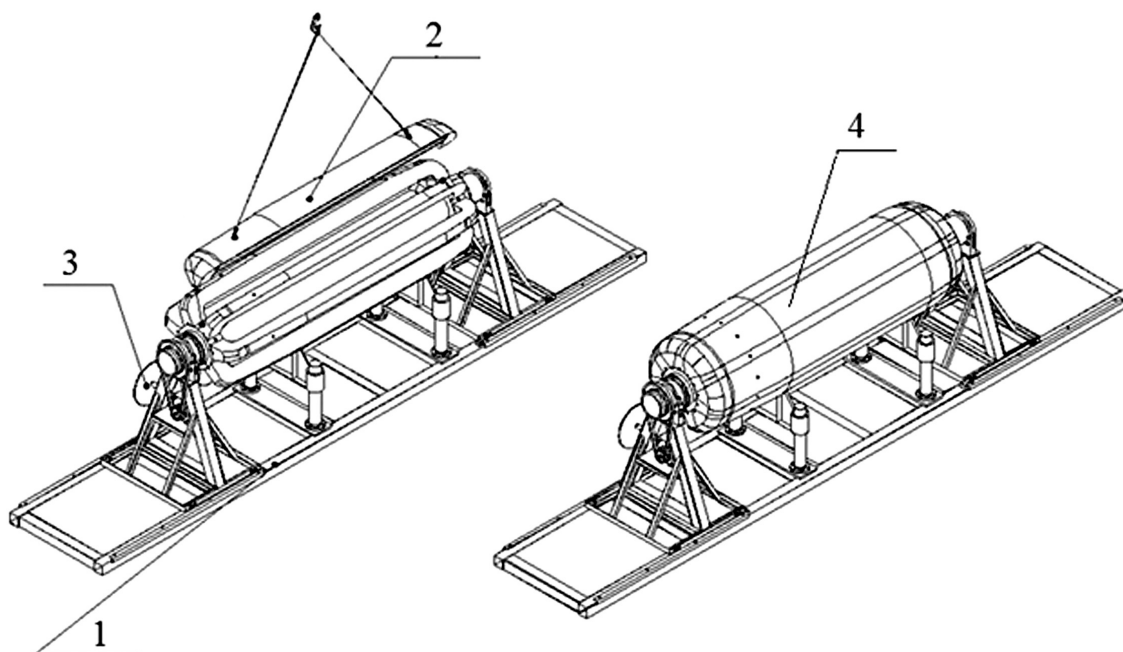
Оправка для изготовления корпуса ракетного двигателя твердого топлива из ПКМ:
